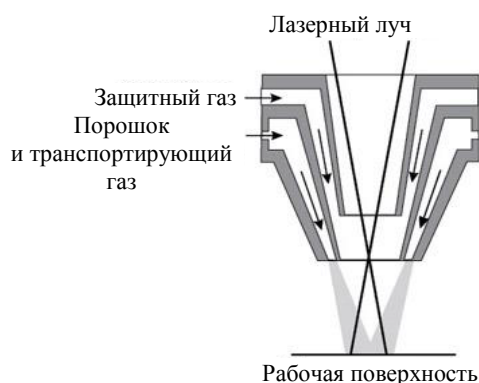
Схема подачи присадочного материала в ванну расплава при лазерной наплавке
